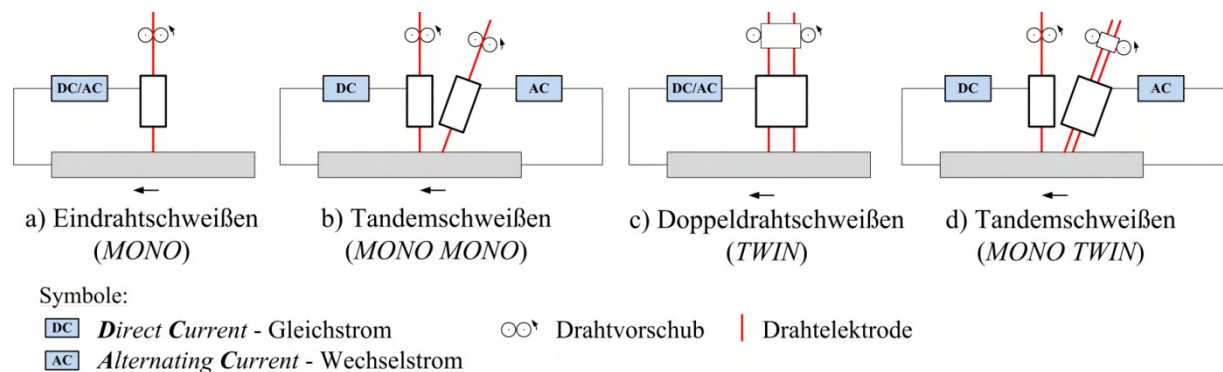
Gängige Verfahrensvarianten für das UP-Schweißen (ESAB)
